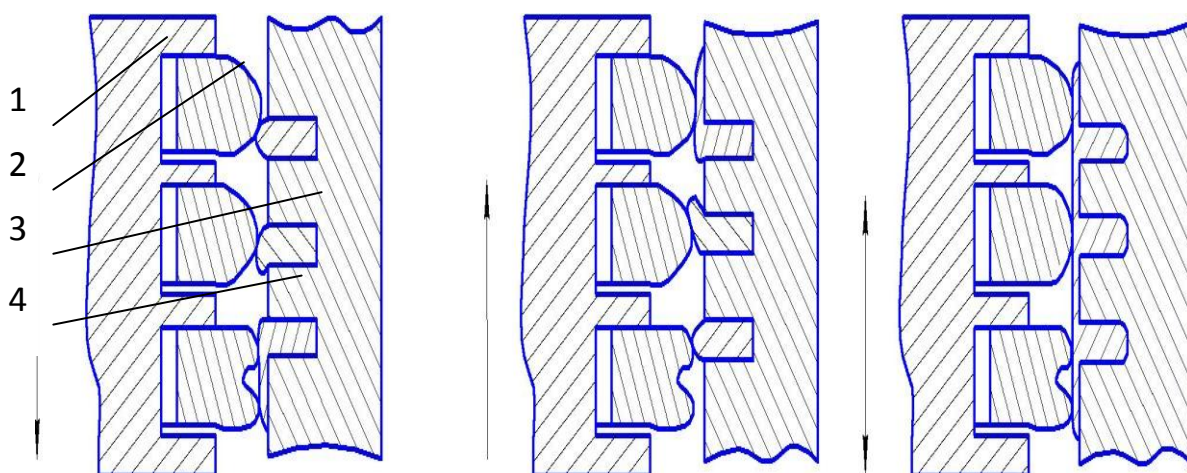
Схема образования плёнки на поверхности гильзы цилиндров: 1- поршень; 2-поршневое кольцо; 3-гильза цилиндров; 4-вставка
